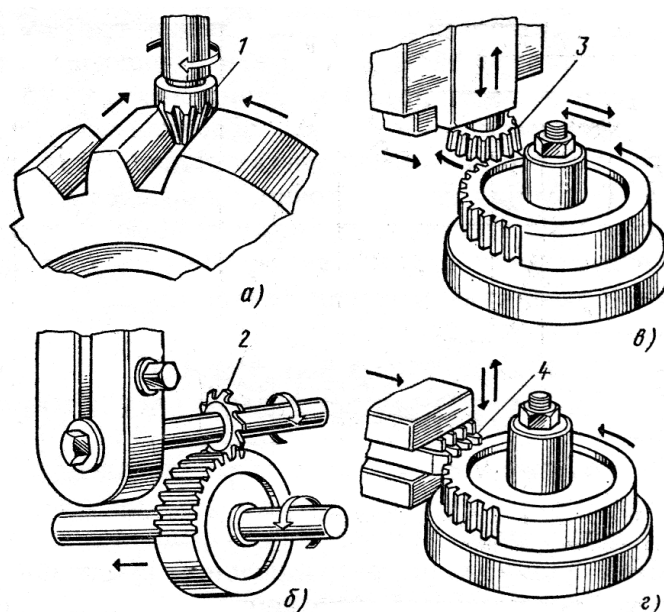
Нарезание зубчатых колес копированием с помощью фрез и обкаткой с помощью долбяка и гребенки:
